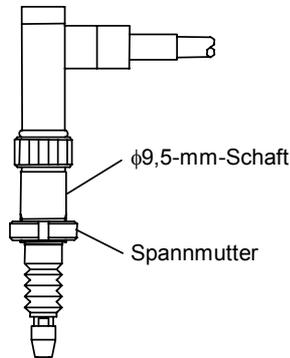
Linear Gage mit 9,5mm-Schaft und Spannmutter
